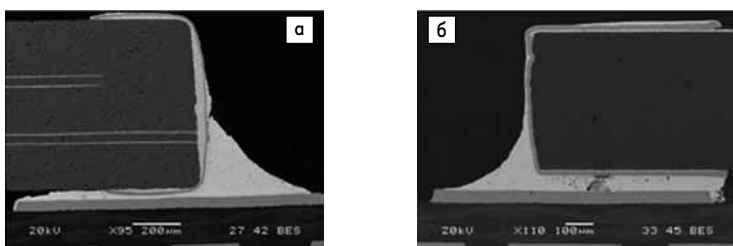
Форма паяных соединений для поверхностного монтажа: а) резистора; б) конденсатора
